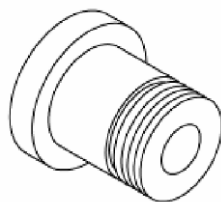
Очистка механизма подачи сварочной проволоки
